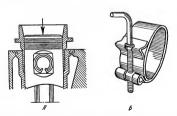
Приспособления для установки поршия с кольцами в цилиндр; а) оправка (в форме стального конусного кольца); б) ленточное.
